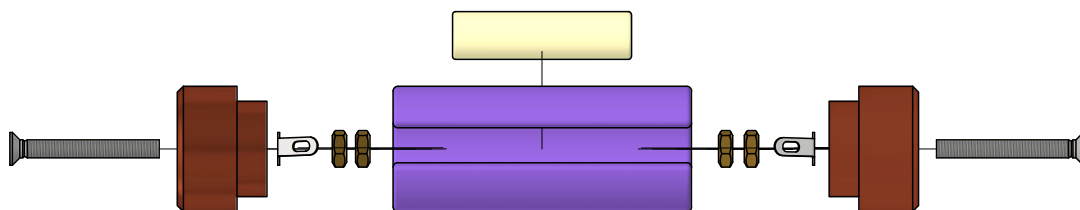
Zelldummy als Explosionszeichnung
